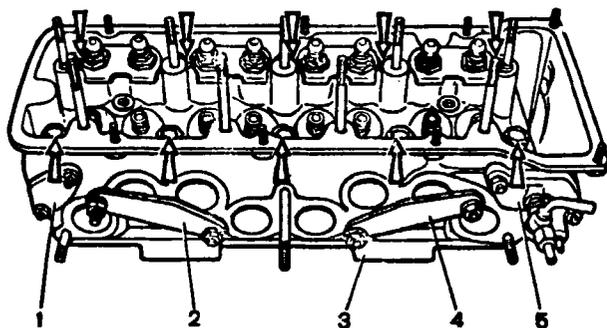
Проверка герметичности головки цилиндров на приспособлении А.60334: 1, 2, 4 - заглушки; 3 - плита приспособления; 5 - фланец со штуцером подвода воды
